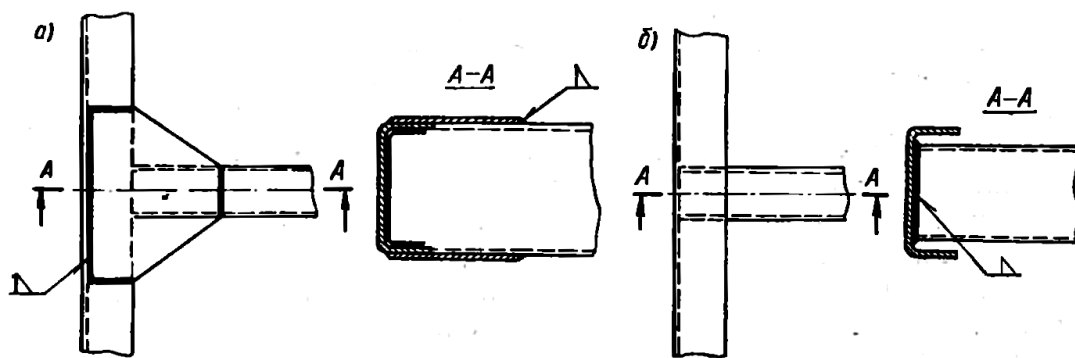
Способ крепления сваркой поперечин закрытого прямоугольного профиля к лонжерону корытного сечения
